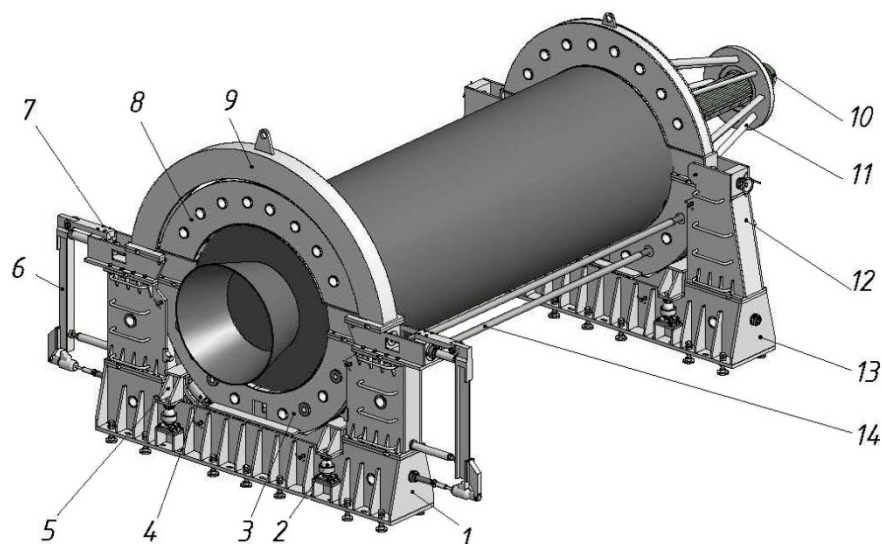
Общий вид универсального стапеля для ОСИ крупногабаритных РДТТ:
